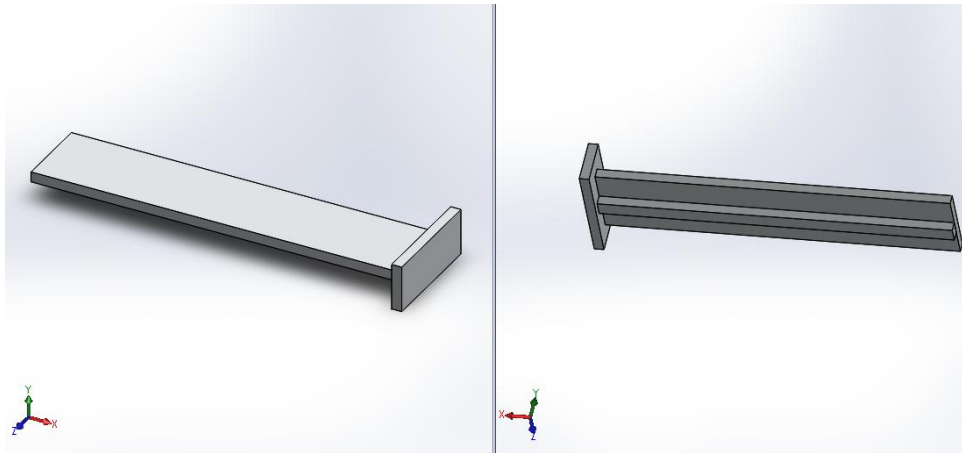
12. Soportes laterales Fuente: diseño propio.
